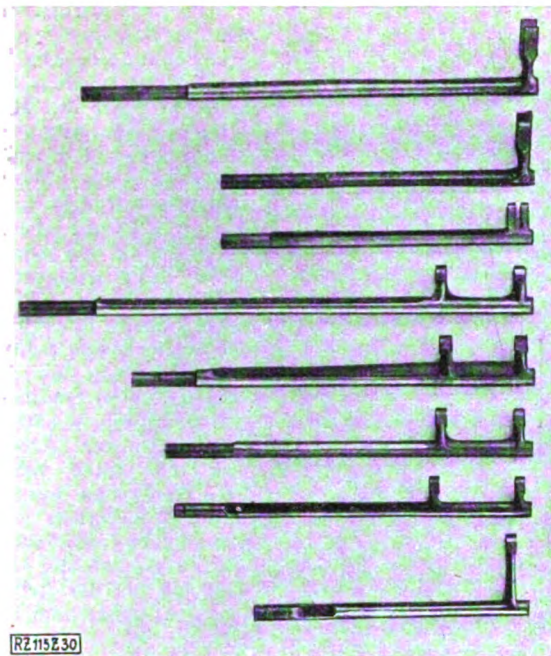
Hebe- und Schiebewellen einer Nähmaschine.
